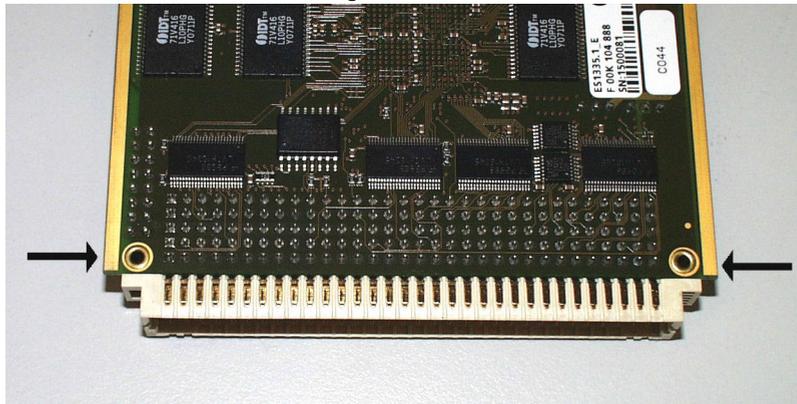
Hohlknoten zur Befestigung der Steckerleiste
